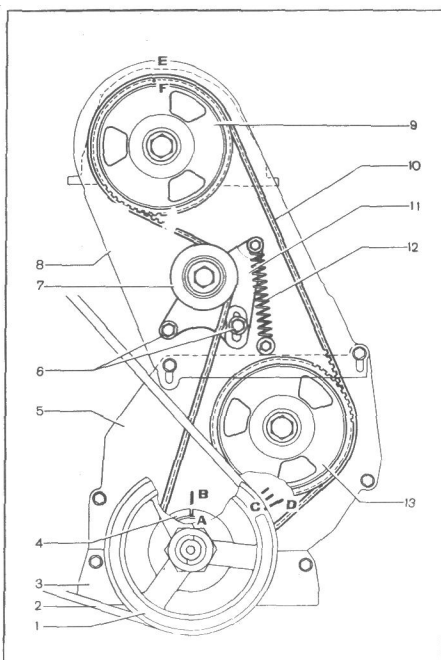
Схема привода механизма газораспределения двигателя ВАЗ-2105: 1 — шкив коленчатого вала; 2 — ремень привода генератора; 3 — нижняя защитная крышка; 4 — зубчатый шкив коленчатого вала; 5 — средняя защитная крышка; 6 — болты крепления кронштейна натяжного ролика; 7 — натяжной ролик; 8 — верхняя защитная крышка; 9 — шкив распределительного вала; 10 — зубчатый ремень; 11 — кронштейн натяжного ролика; 12 — пружина кронштейна; 13 — шкив валика привода масляного насоса
